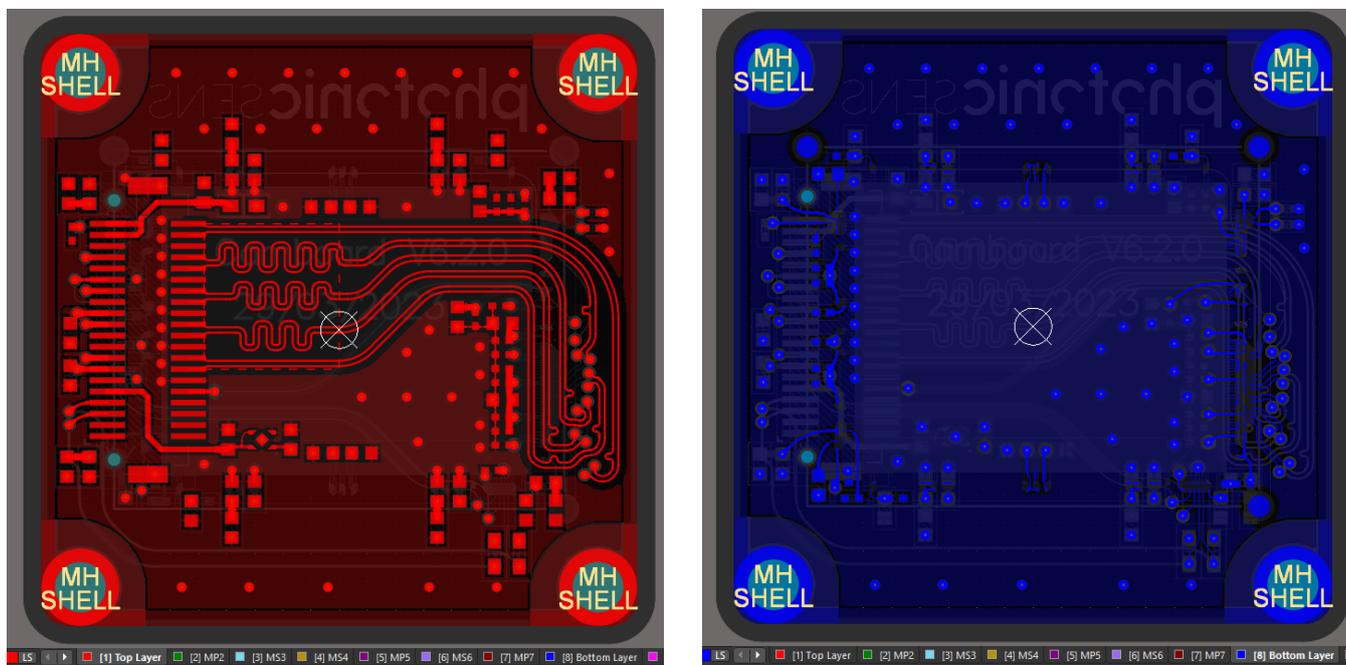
Captura del diseño del PCB Camboard V6.2.0.
